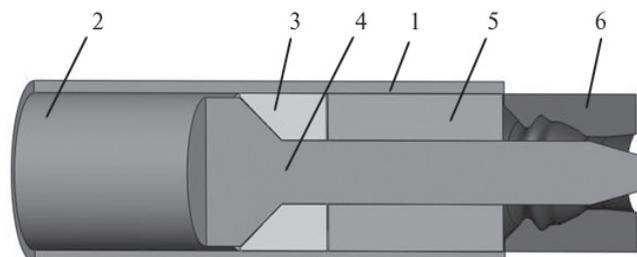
Принципиальная схема прессования трубной заготовки: 1 — контейнер; 2 — пуансон; 3 — пресс-шайба; 4 — игла; 5 — заготовка; 6 — матрица
